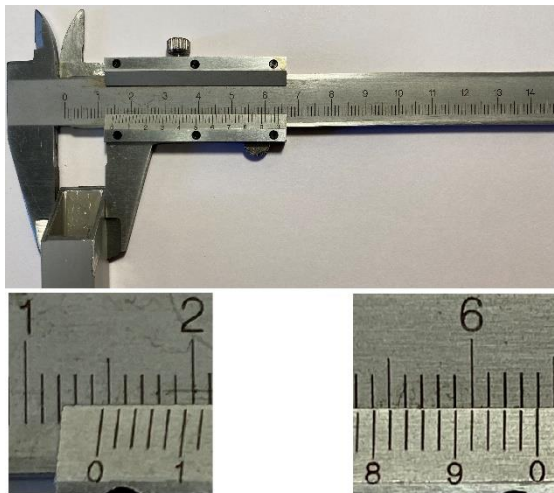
Приклад вимірювання лінійного розміру зовнішніх габаритів.
